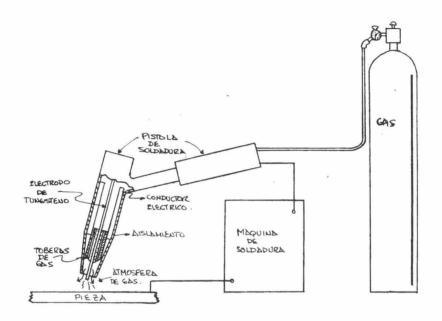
Procedimiento de Soldadura con Arco de Tungsteno - gas.
